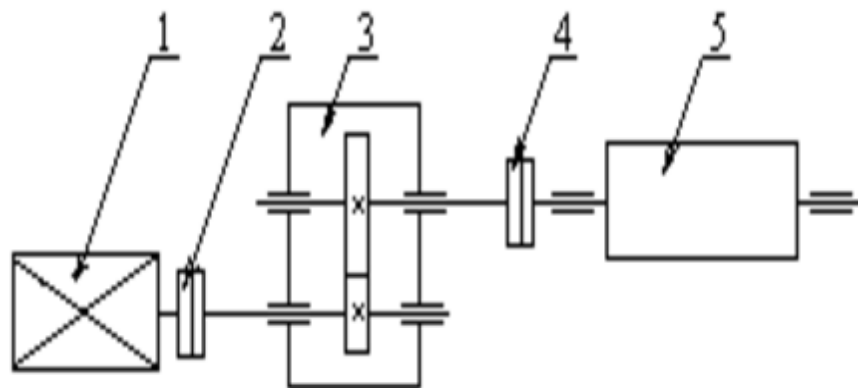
Кинематическая схема: 1 – электродвигатель; 2,4 – зубчатая муфта; 3 – цилиндрический редуктор; 5 – ролик
